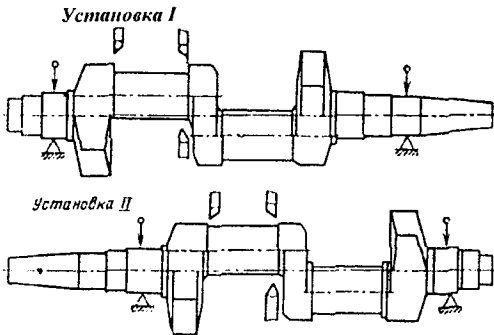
Схема попередньої обробки шатунних шийок колінчастого валу уніфікованого поршневого компресора УУ-220 на багаторізцевому верстаті.
